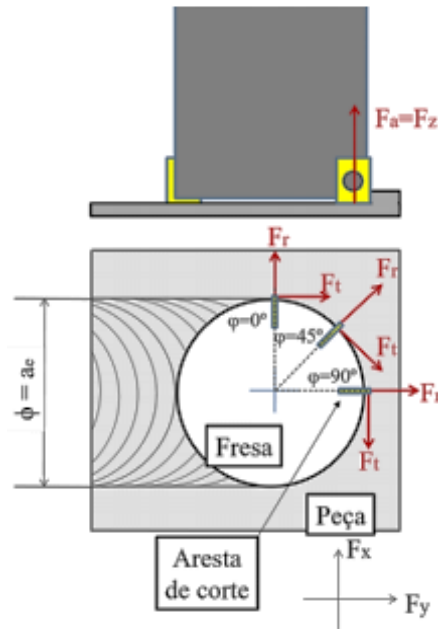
Componentes das forças de usinagem no fresamento frontal [Sória, 2016].
